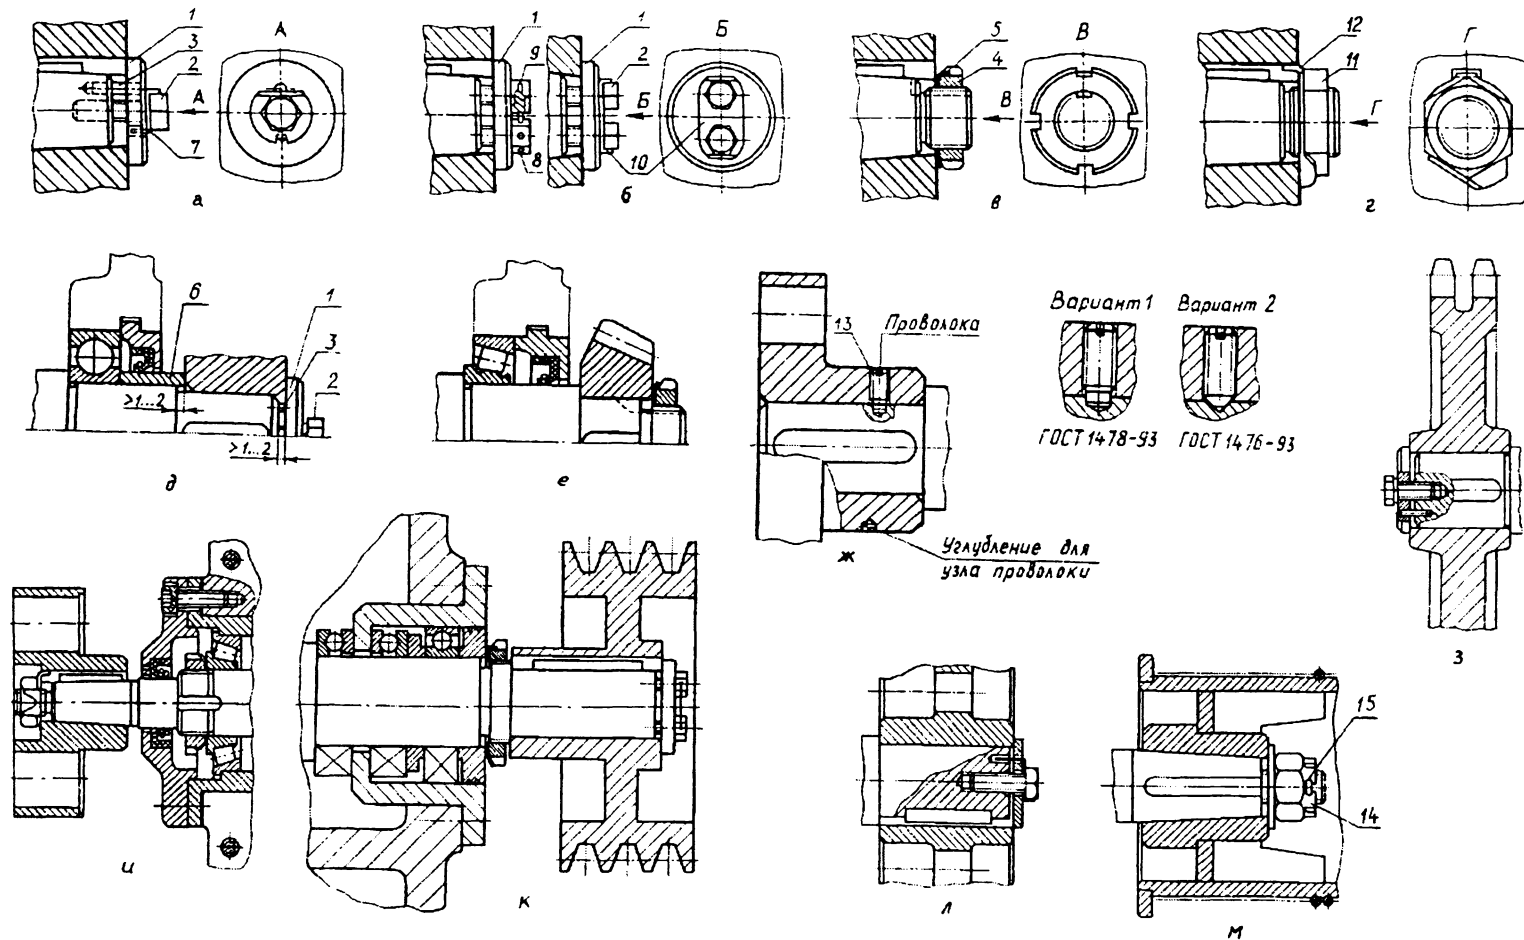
Способы закрепления деталей на концевых участках валов:
